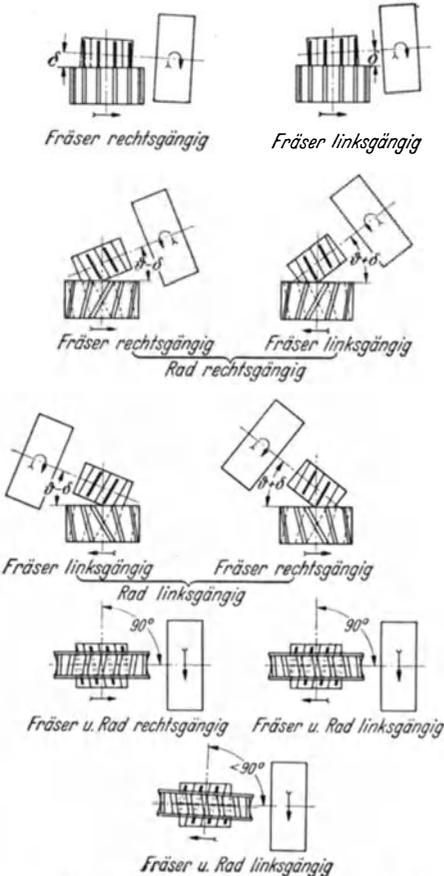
Lage des Fräasers zum Rad beim Fräsen mit Wälzfräser. (Nach GLÄSER.)
